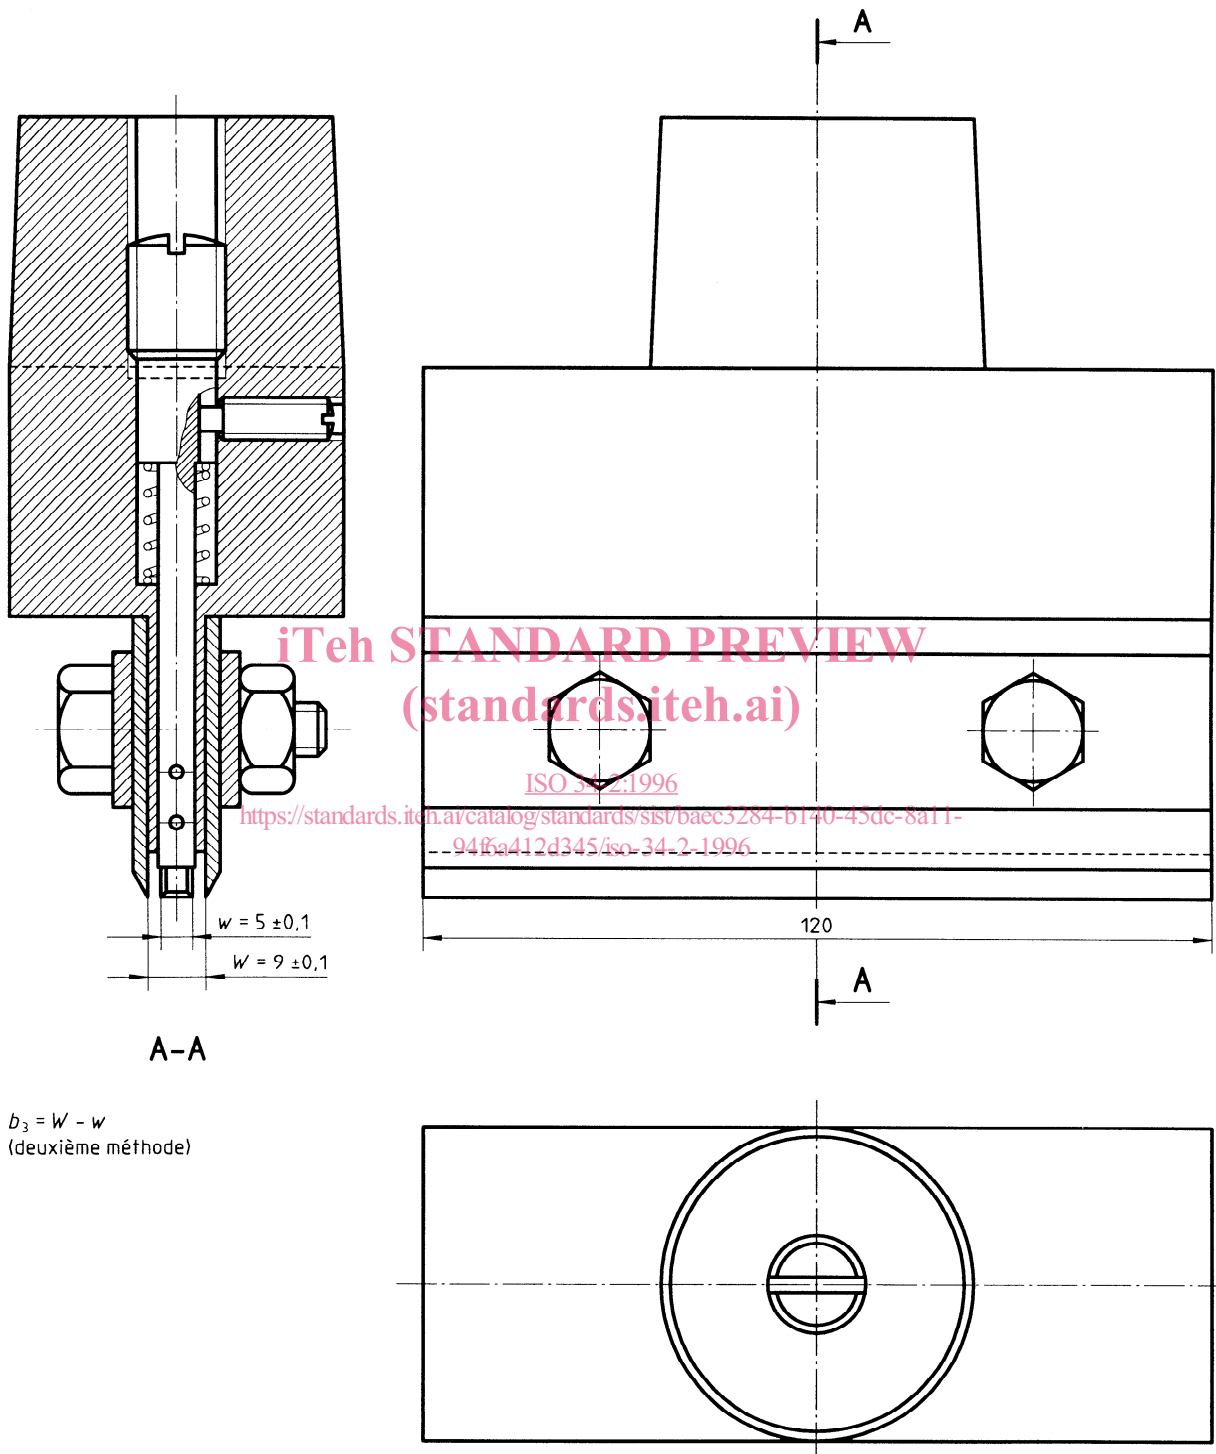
Emporte-pièce pour l'éprouvette de Delft
